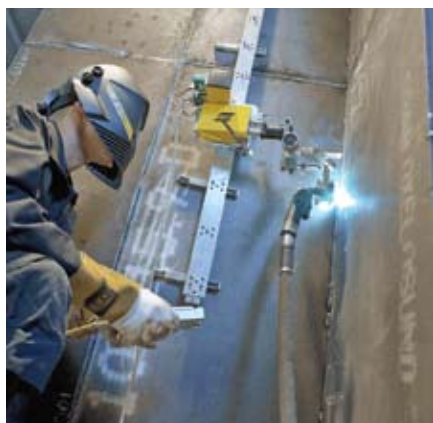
Сварка вертикального углового шва комплексом Kemppi – Railtrac 1000 (направляющий рельс с магнитным креплением)
